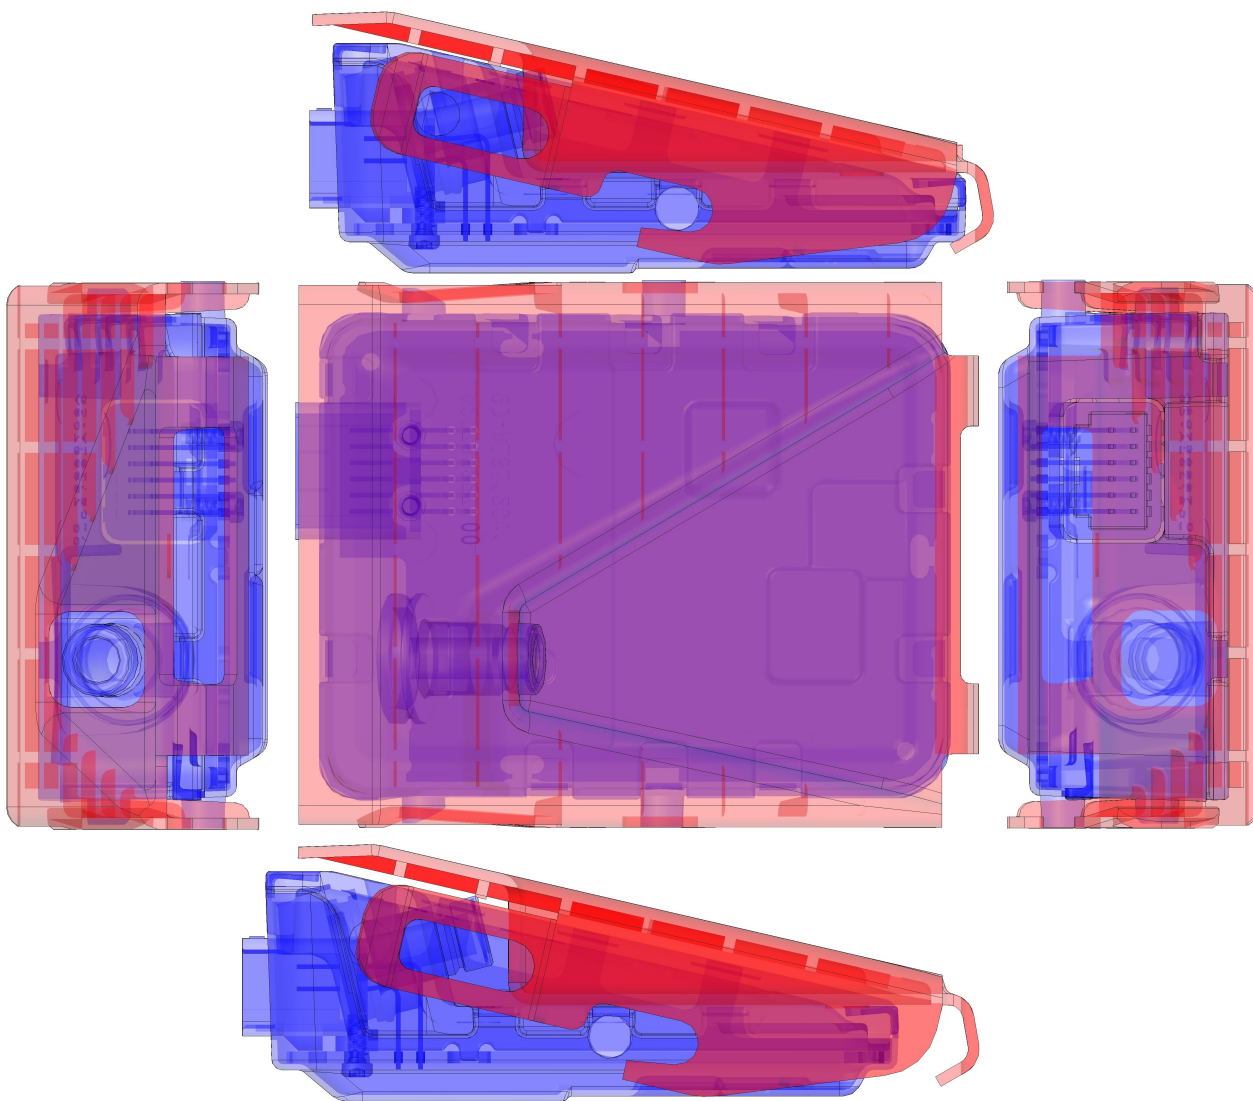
Varianta constructivă a IV-a a bracketului (suportului) pentru camera video fixată pe parbrizul automobilului
